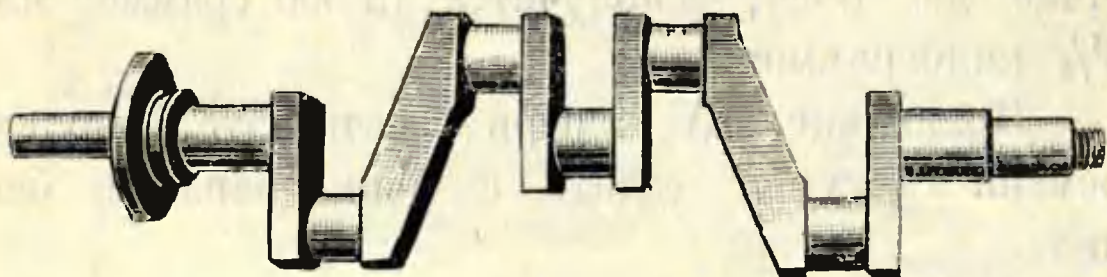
Коленчатый вал, выточенный из одного куска очень хорошей стали.
